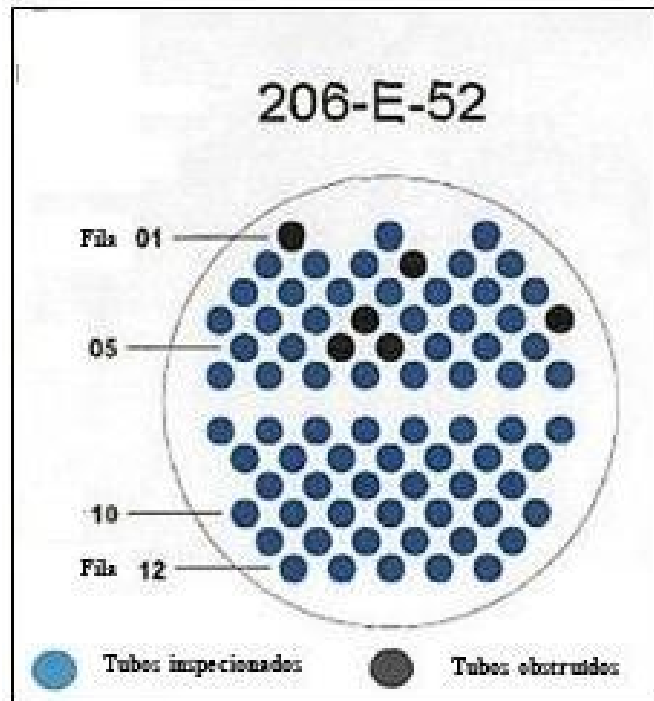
Desenho do ensaio ultrassônico para medição da espessura.
